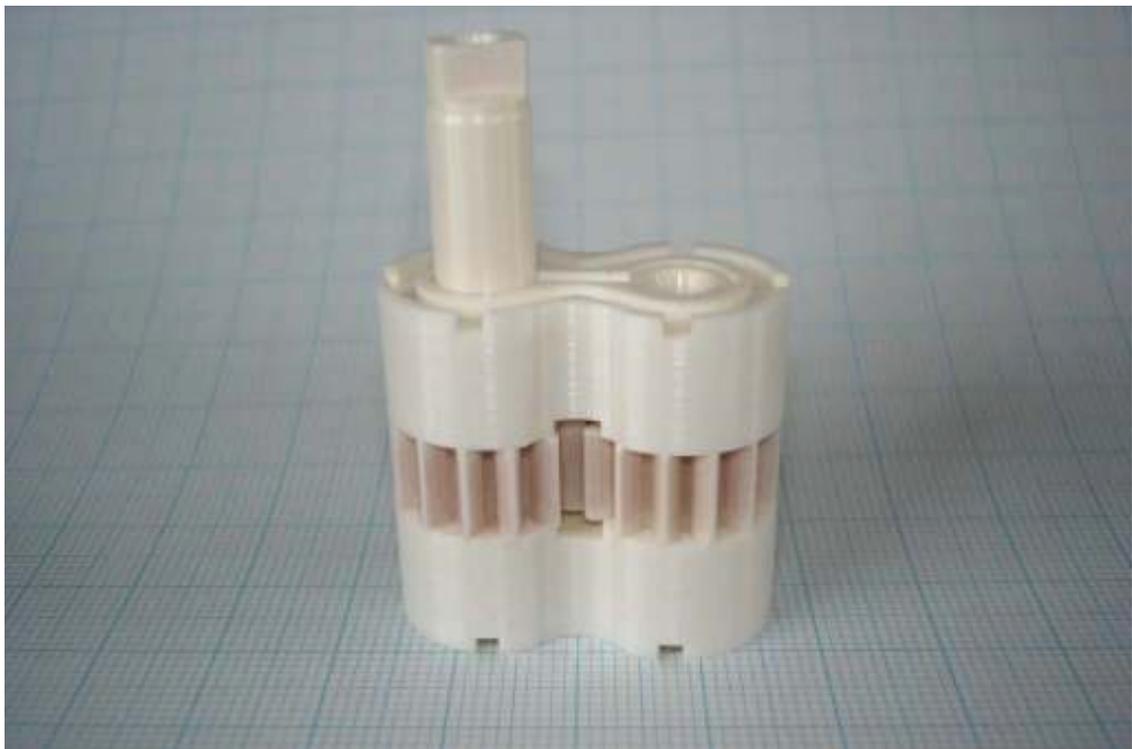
Zahnradgruppe für Pumpe aus ZrO_2 Y-TZP
